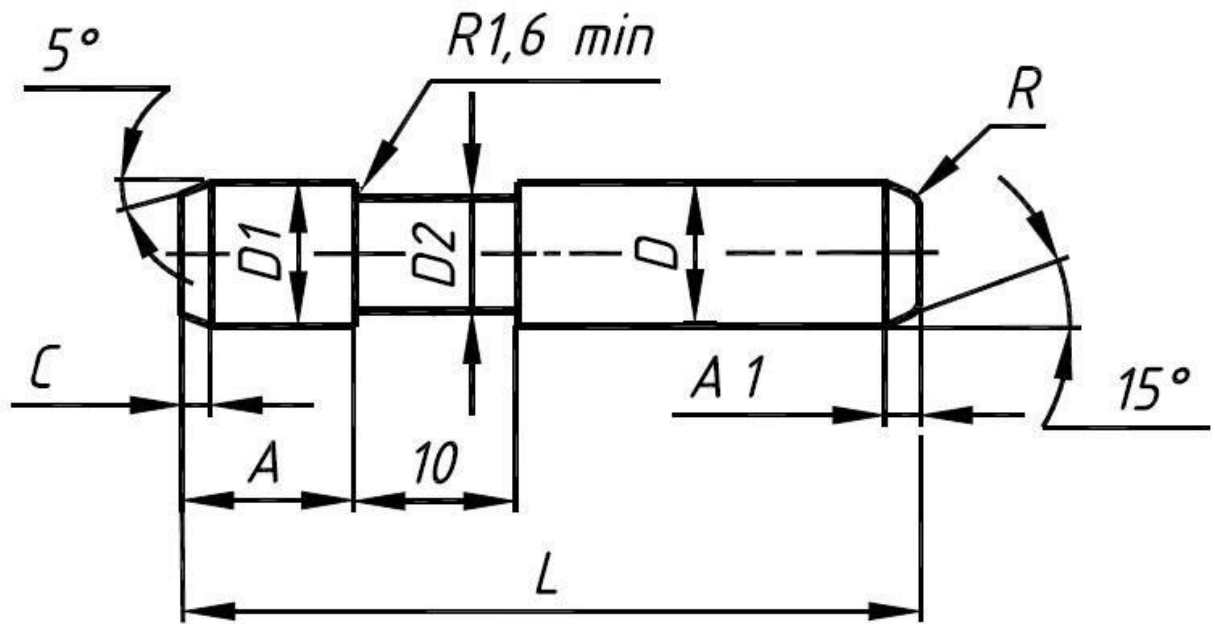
Чертеж с параметрами ступенчатой колонки блока штампа.
